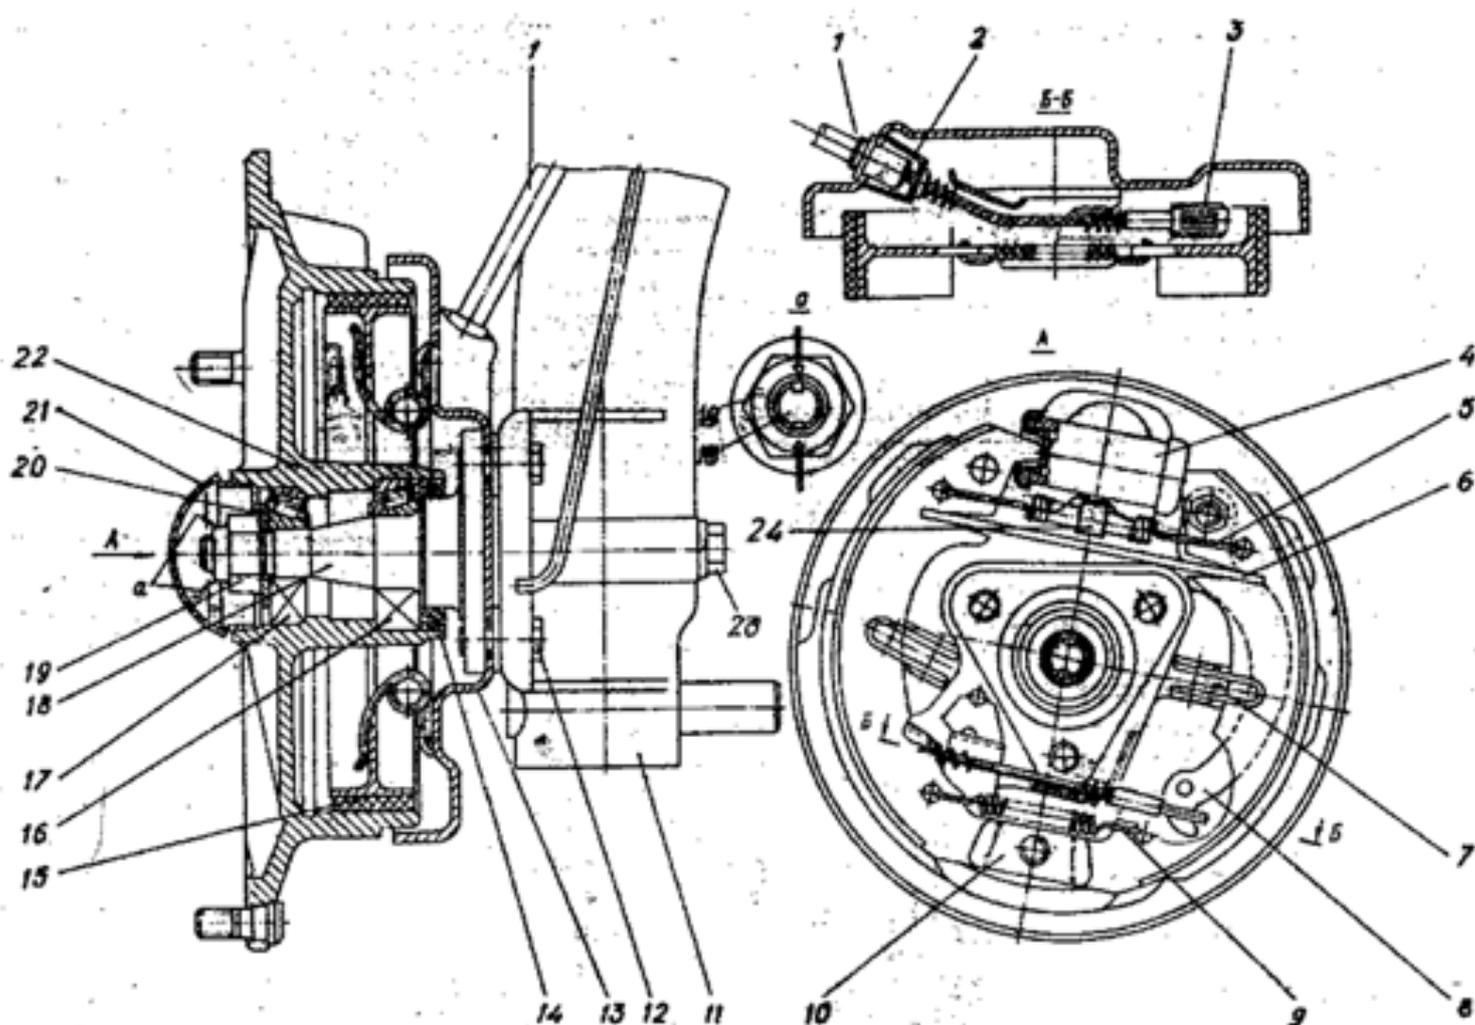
Задняя подвеска и задний тормоз: 1 - трос стояночного тормоза; 2 - упор троса; 3 - наконечник троса; 4 - цилиндр колесный; 5 - пружина стяжная верхняя; 6 - планка распорная; 7 - пружина колодок; 8 - рычаг разжимной; 9 - пружина стяжная нижняя; 10 - опора колодок; 11 - балка задней подвески; 12 - болт короткий крепления ступицы; 13 - щит тормоза; 14 - сальник; 15 - колодка тормоза; 16 - подшипник внутренний; 17 - подшипник наружный; 18 - ступица; 19 - гайка ступицы; 20 - шайба запорная; 21 - колпак; 22 - тормозной барабан.
